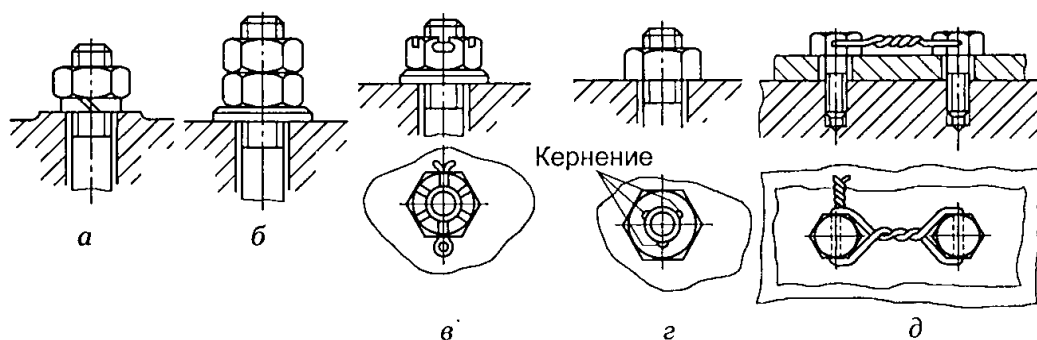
Способы стопорения крепежных деталей: а — пружинной шайбой; б — двумя гайками; в — шплинтами; г — приваркой или кернением; д — проволокой
